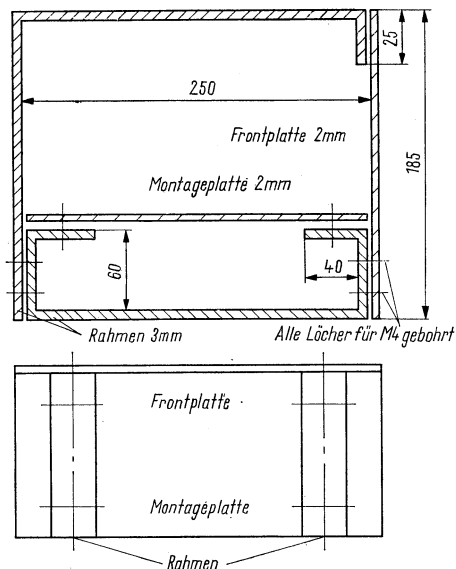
Universalchassis, bei dem Frontplatte und Aufbauchassis durch 2 Rahmen gehalten werden
